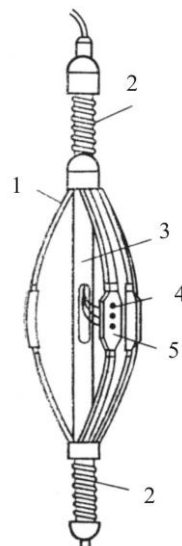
Микрозонд с рессорным прижимным устройством: 1 - рессора, 2 - пружина, 3 - корпус, 4 - электроды, 5 - башмак
